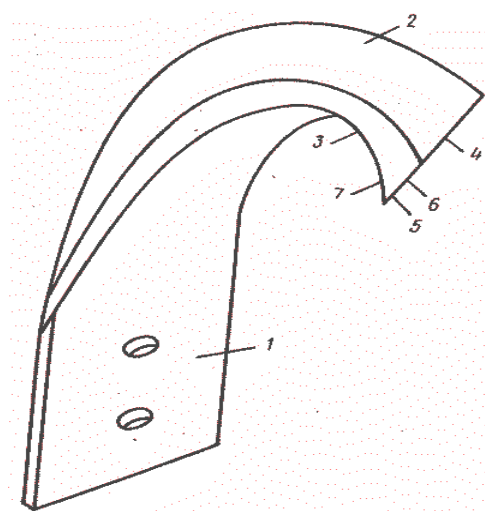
Нож почвообрабатывающей фрезы
